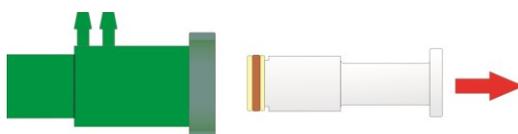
Extraer el elemento de remolino con la herramienta de montaje
